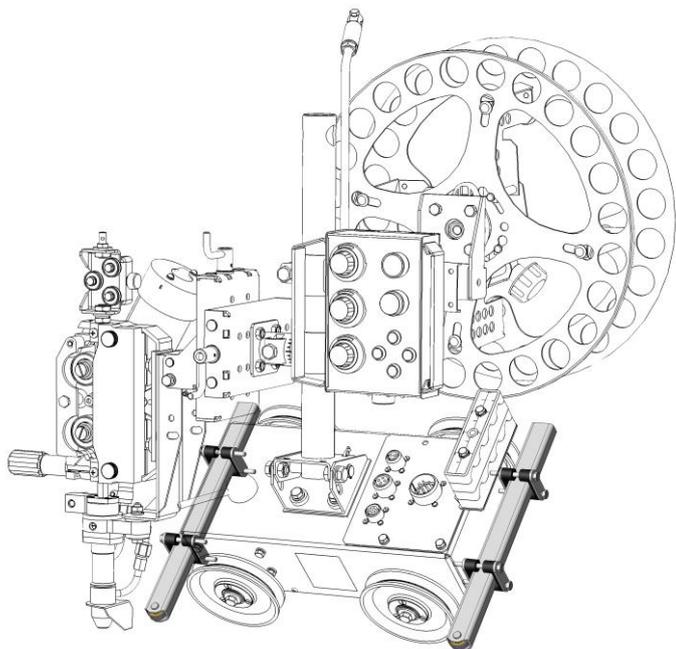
Комплект упоров для сварки «в лодочку».
